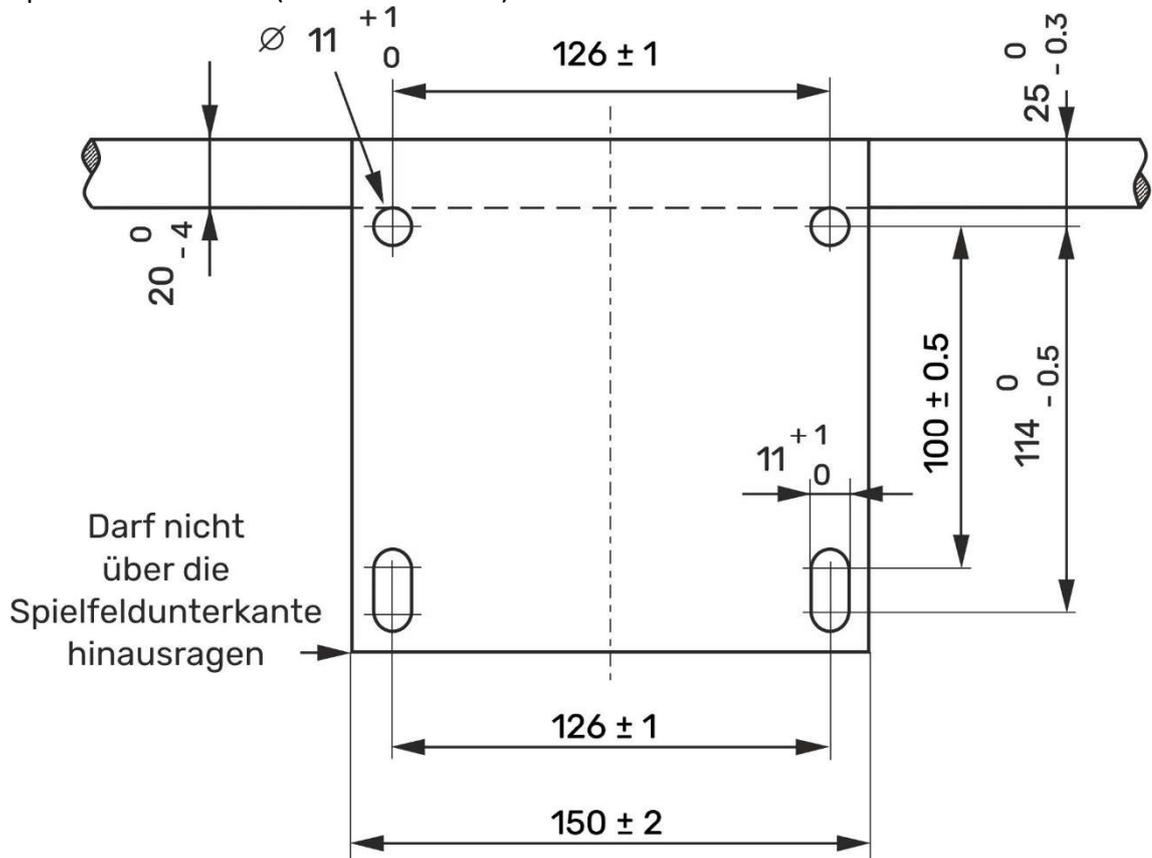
Montageplatte des Rings (Maßangaben sind Beispiele)
